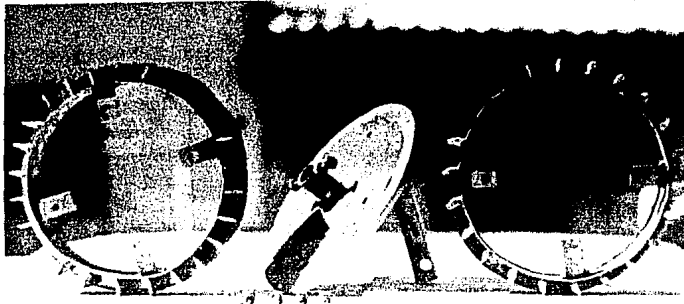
Conjuntos que forman el dosificador C; lado X (derecha); lado Y (izquierda).
